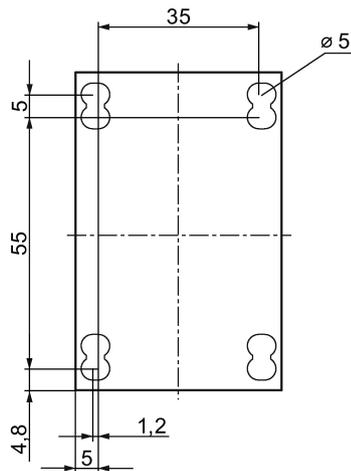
Bohrplan der Schütze in Federzuganschlusstechnik (Baugröße S00)
